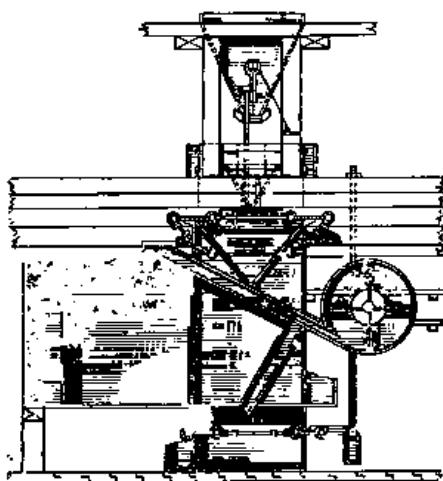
Схема веичної установки конструкции Ушкова.
